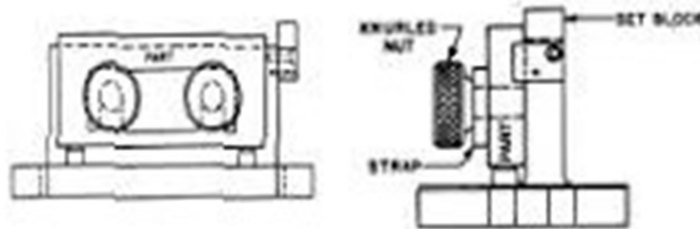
Fixture Plat (Plate Fixture)
